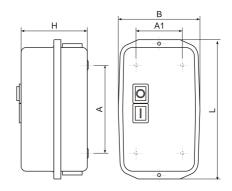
Пускатели ПМ12-040/ПМ12-063 в металлическом защитном корпусе со степенью защиты IP54.
